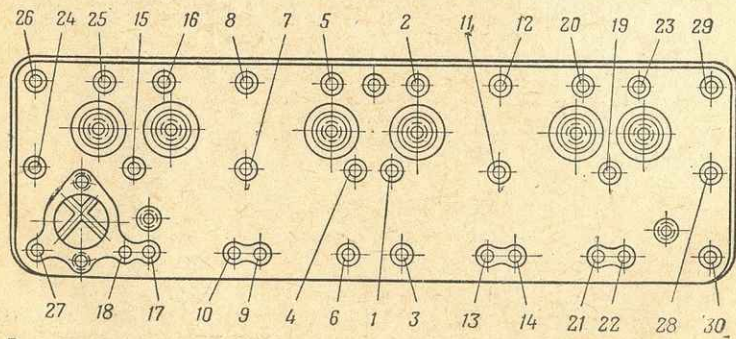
Последовательность затяжки болтов и гаек крепления головки блока цилиндров
